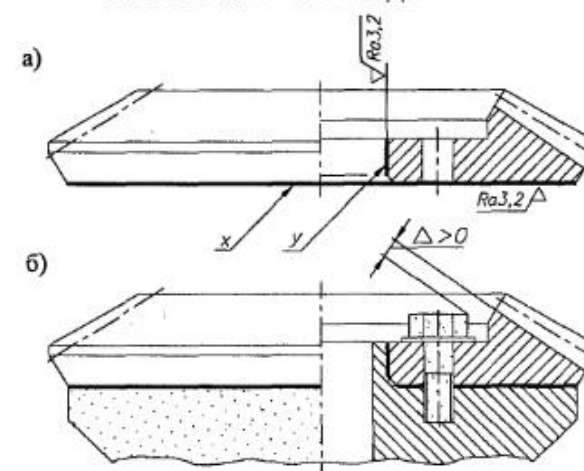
Установочные базы для нарезания зубьев на колесах-дисках
